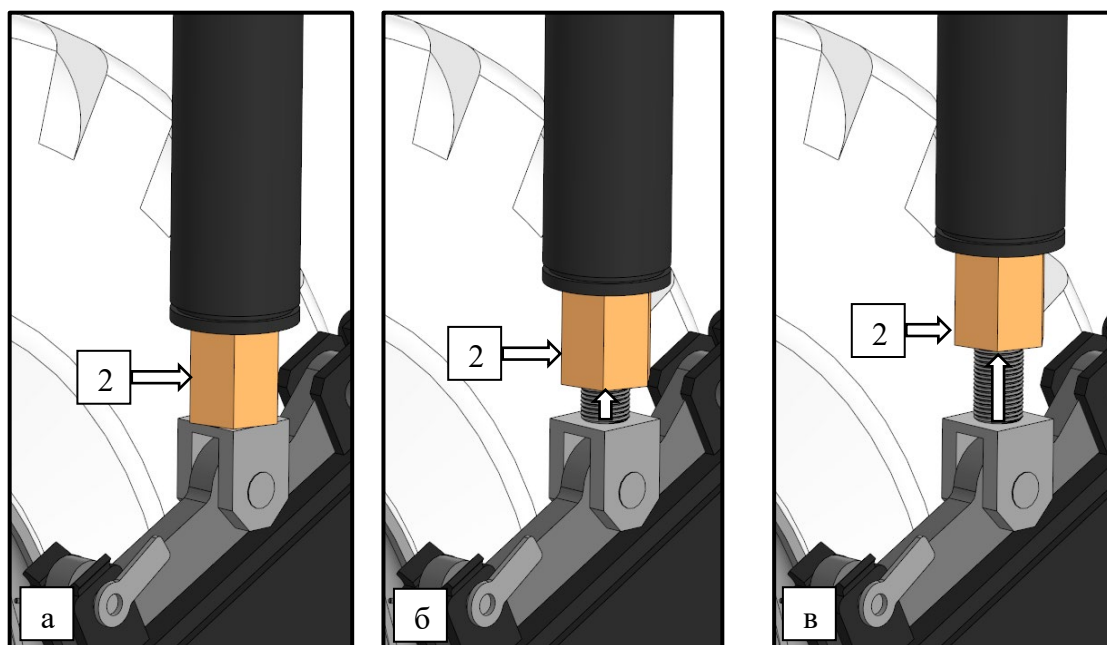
Регулировка упорной гайки на гидроцилиндрах:
